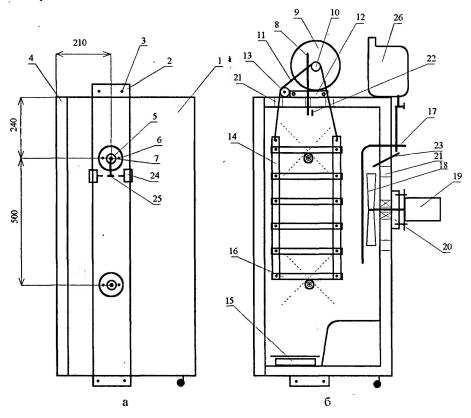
Корпус инкубатора из холодильника. Общий вид
